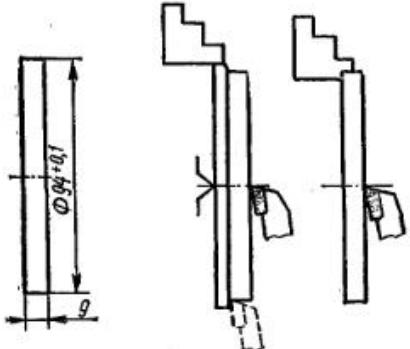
Обработка точного по диаметру диска из штучной заготовки
